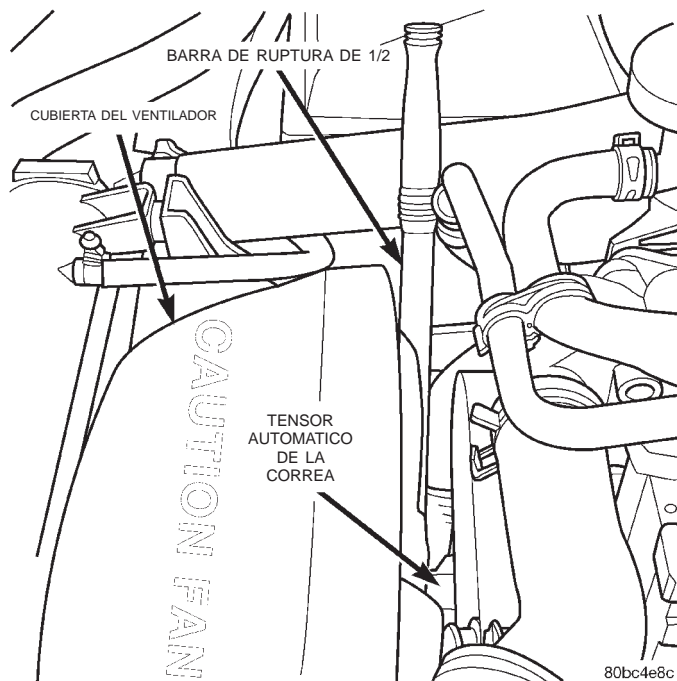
Desmontaje de la correa de transmisión de accesorios
